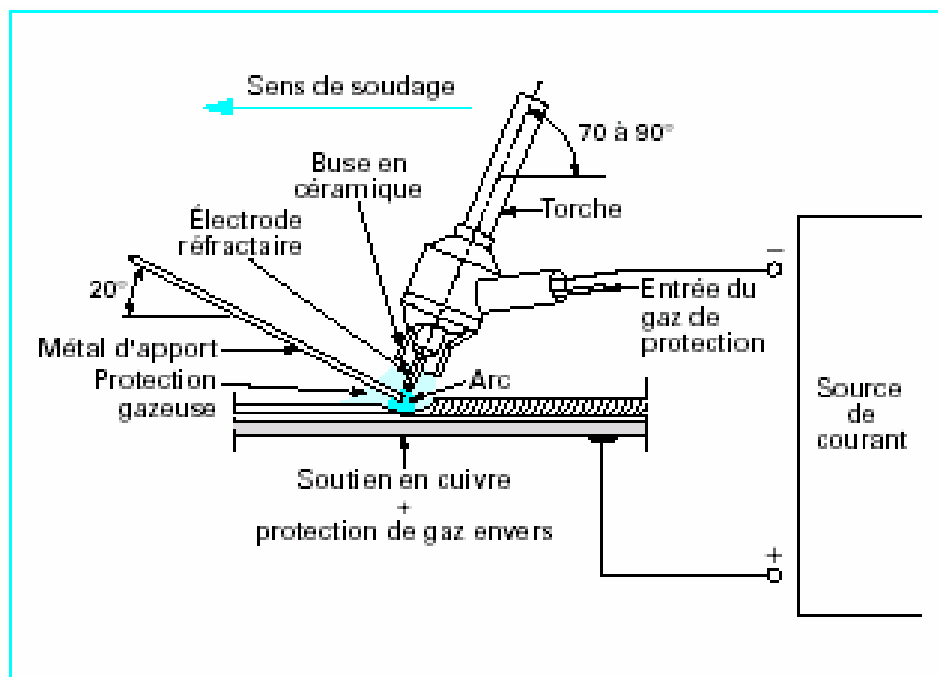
Principe du soudage à l'électrode réfractaire TIG manuel [20].
